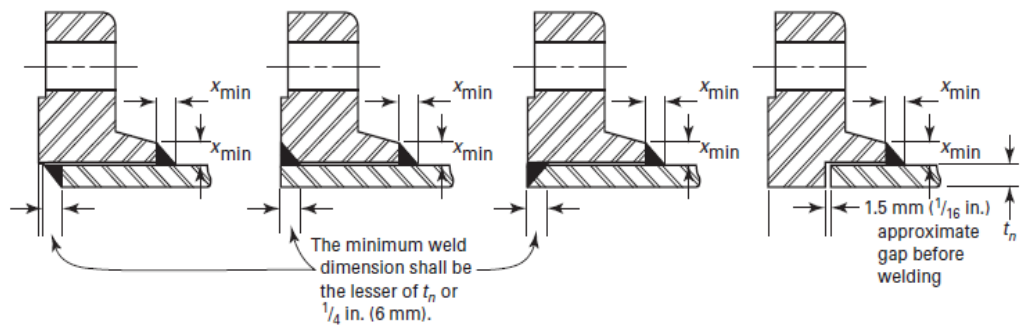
Criterio de soldadura para Brida Slip-On
